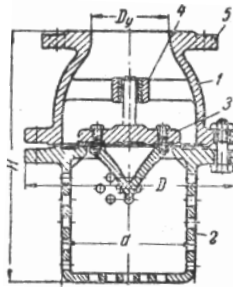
Клапан приймальний фланцевий 16ч42р.
